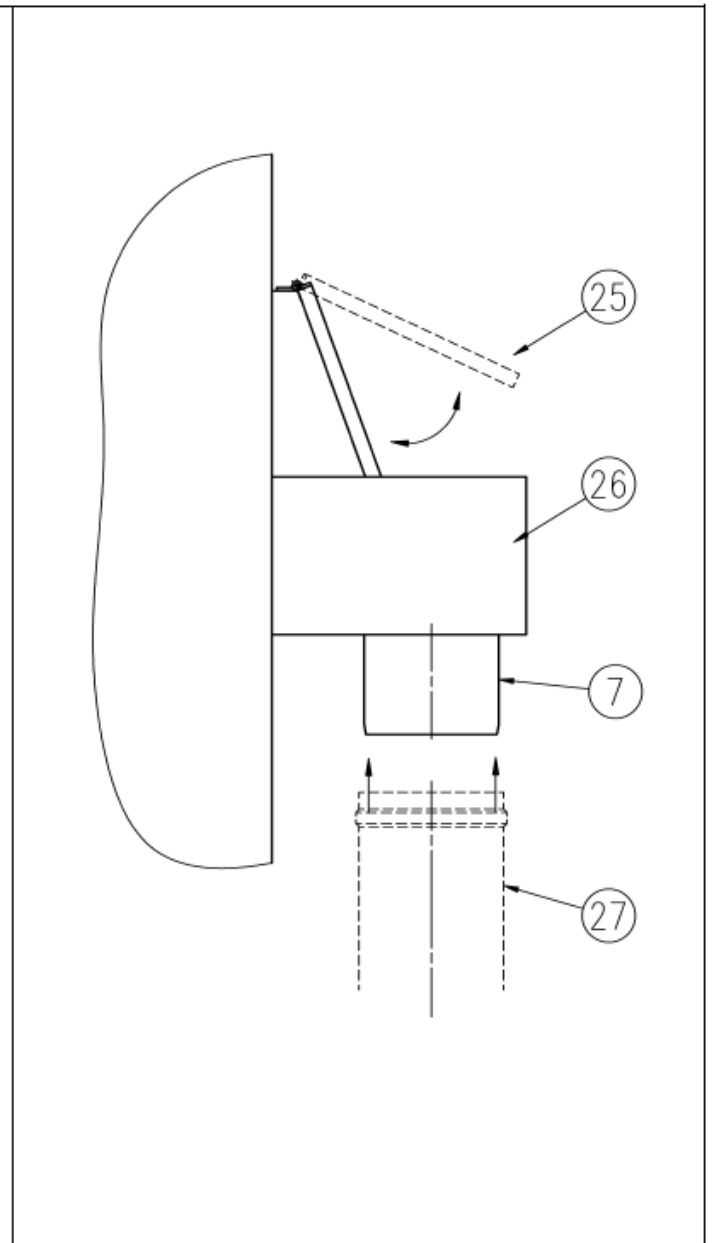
Поплавковый выключатель для низкого уровня воды:
